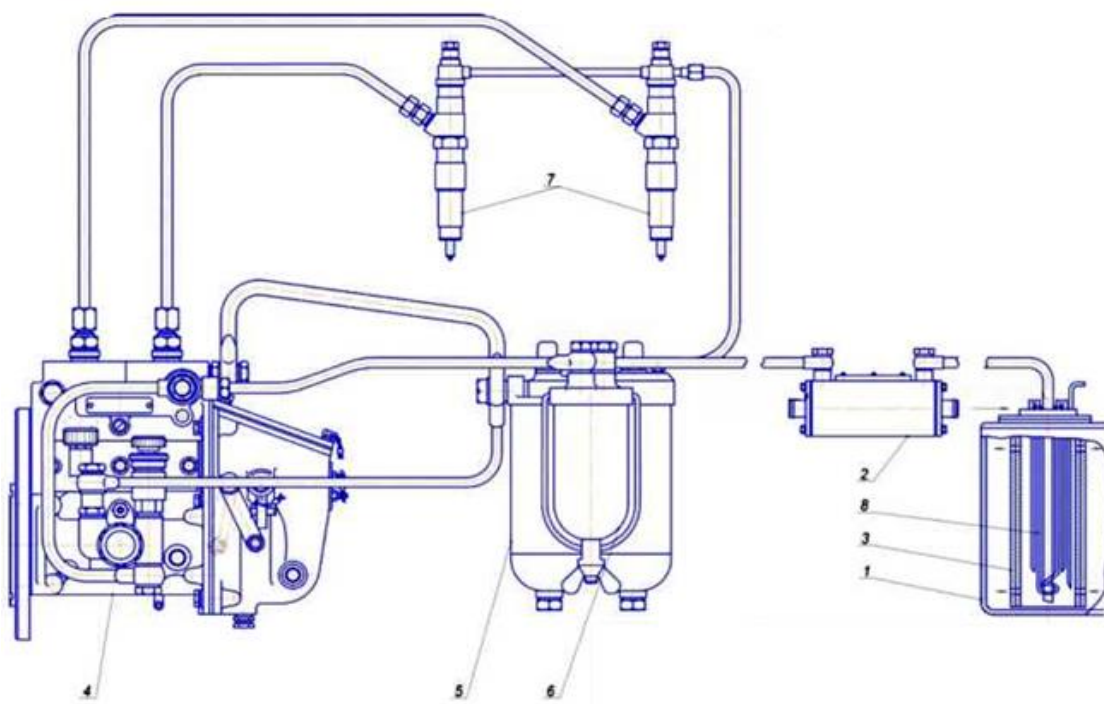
Конструкція системи паливоподачі двигуна, який працює на біопаливі (ріпаковій оливі): 1 – бак; 2 – нагрівач оливи; 3 – камера нагрівання; 4 – паливний насос високого тиску; 5 – фільтр паливний тонкої очистки; 6 – фільтр паливний грубої очистки; 7 – форсунки; 8 – нагрівальний елемент.
